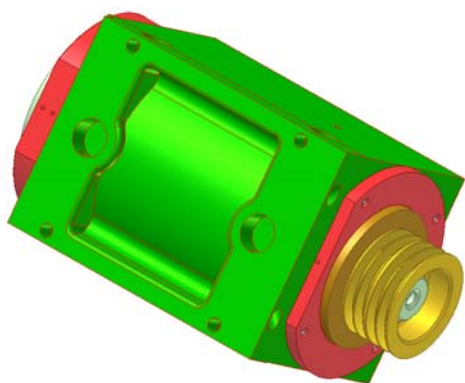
Сборочный узел «Головка отделочно-расточная».
